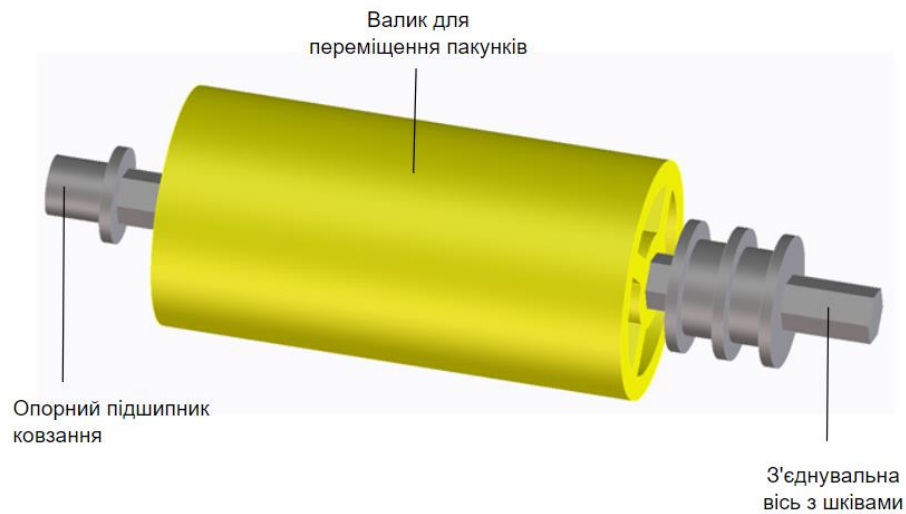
Конструкція одного ролику в поєднанні з елементами кріплення
